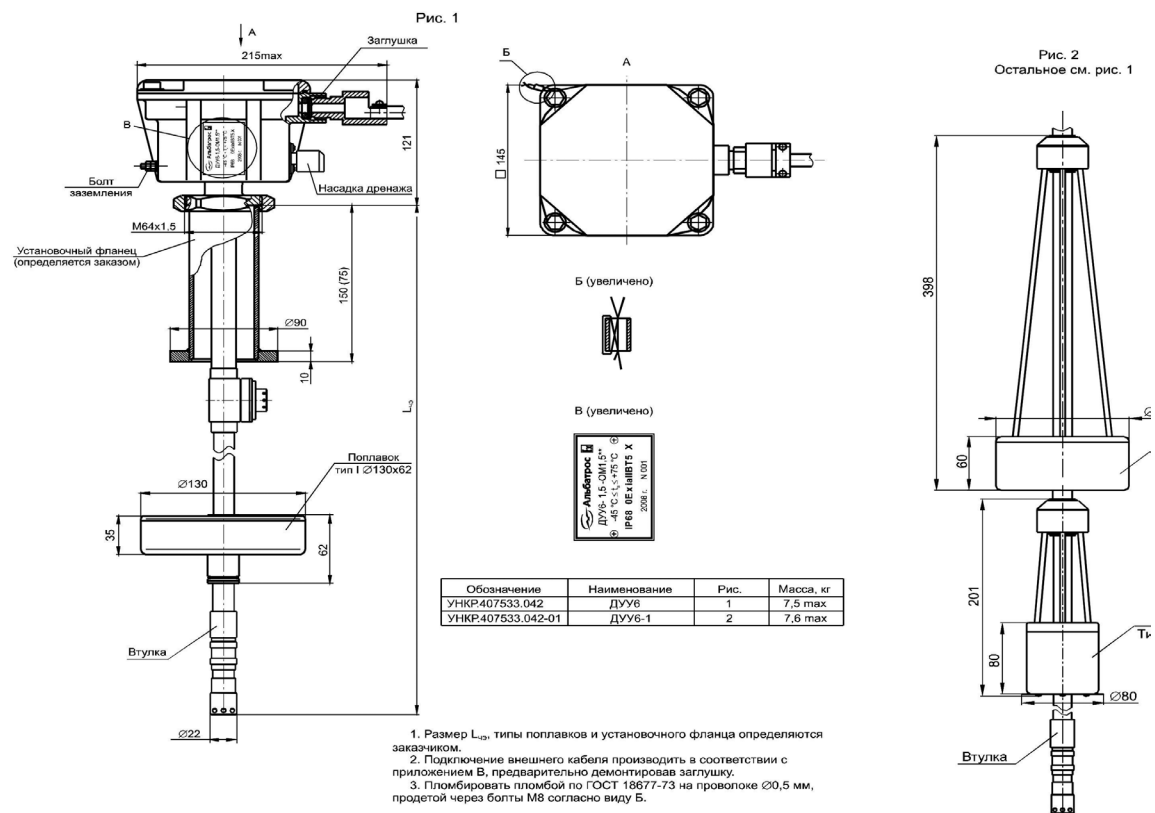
Габаритные размеры датчиков ДУУ6 (ДУУ6-1)
